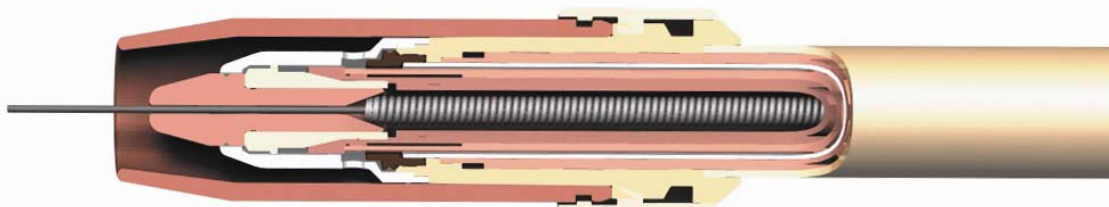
Сечение головки горелки для сварки МИГ/МАГ
